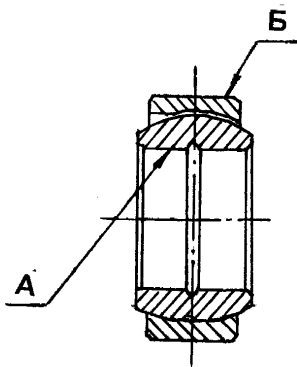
Подшипник шарнирный ШС25 насоса ОПВ2–110кэ
